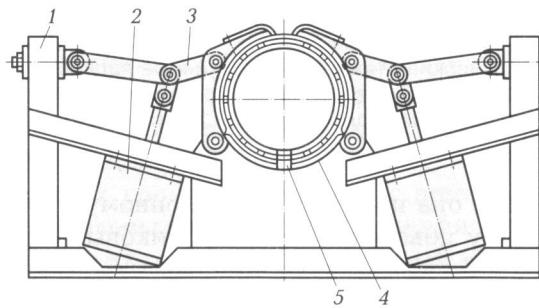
Приспособление для сборки по продольным стыкам обечаек малого диаметра:
